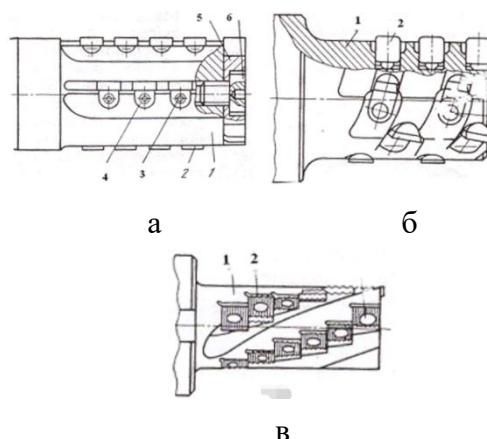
Схемы концевых фрез с перекрытием по образующей цилиндра (а), по винтовой линии (б) и с тангенциальным расположением режущих пластин (в): 1 – корпус; 2 – режущие пластины; 3 – винт; 4 – клин; 5 – диск; 6 – стопорный винт
